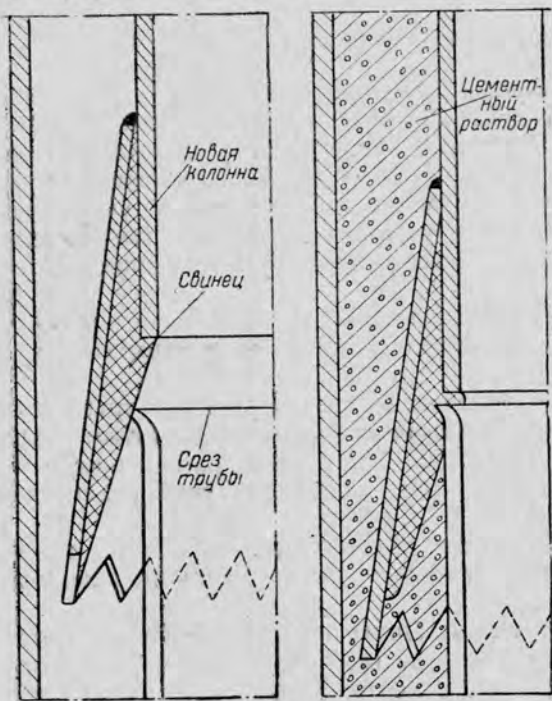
Башмак для установки новой колонны на срез обсадной трубы.
